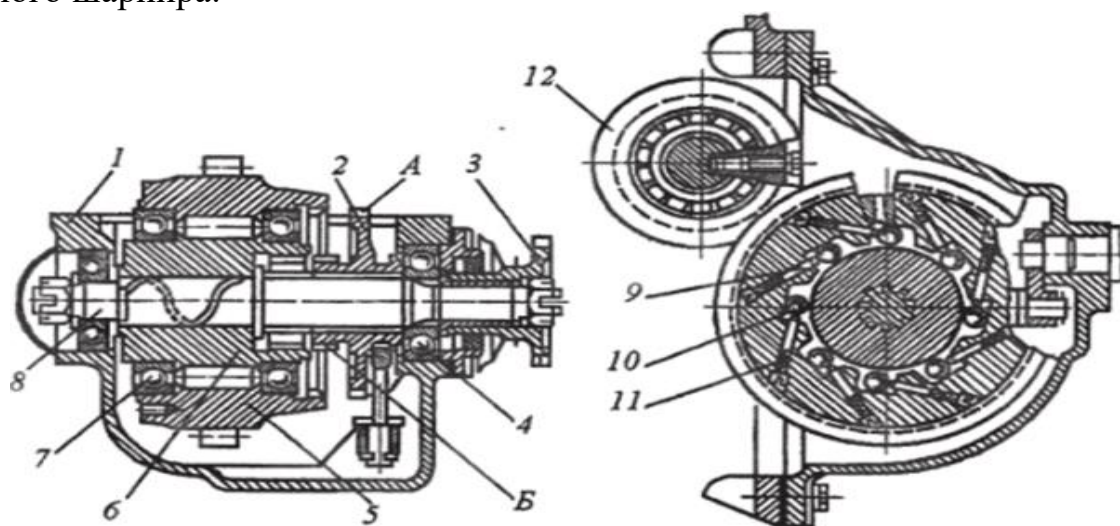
Раздаточная коробка трактора МТЗ-82:
